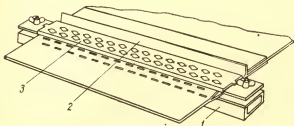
Приспособление для стыковки конвейерных лент с помощью П-образных скоб:
